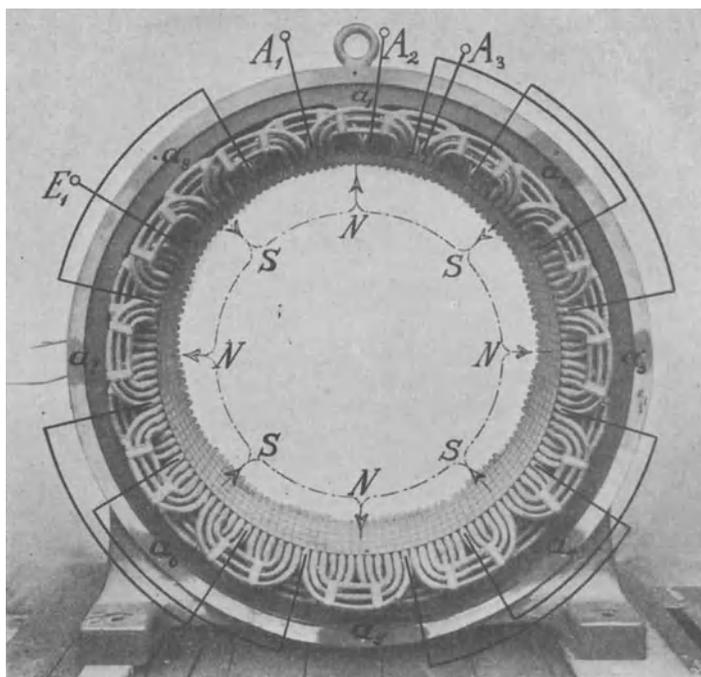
8poliger Ständer einer Drehstrommaschine.
